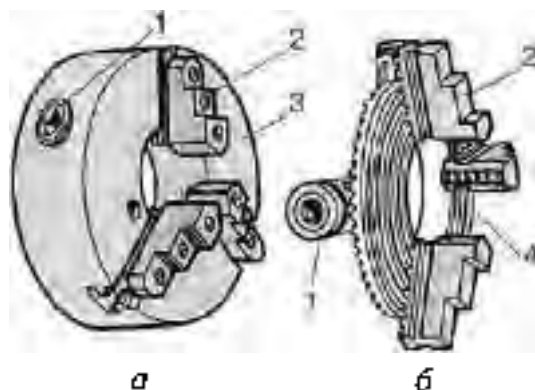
Трикулачковий самоцентрувальний патрон
